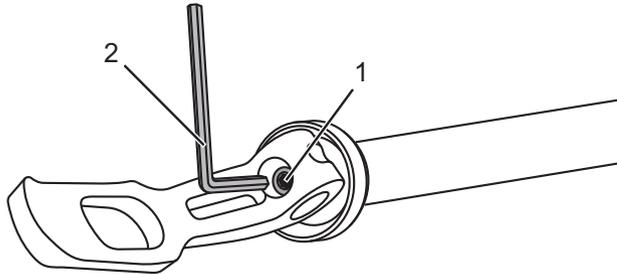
Regolazione della forza di serraggio al centro della leva di serraggio (1) mediante la chiave a brugola (1) applicata alla leva di serraggio (2)
